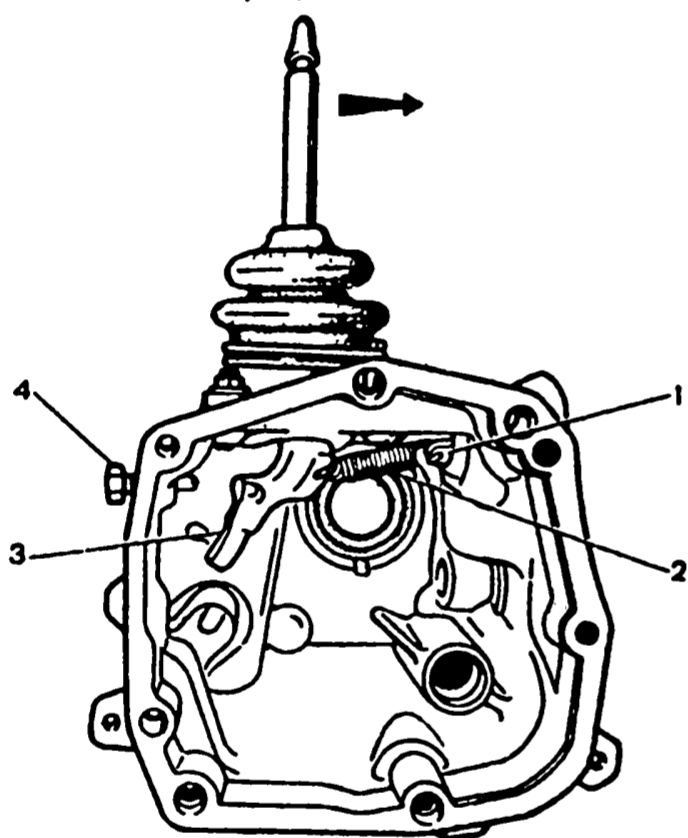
Внутренний вид задней крышки коробки передач: 1 - винт с ушком крепления оттяжной пружины рычага переключения передач; 2 - оттяжная пружина рычага; 3 - рычаг переключения передач; 4 - винт ограничения поперечного хода рычага. Стрелкой указано направление, в котором нужно переместить рычаг, чтобы вывести его из зацепления с головками штоков переключения передач и снять заднюю крышку коробки передач
